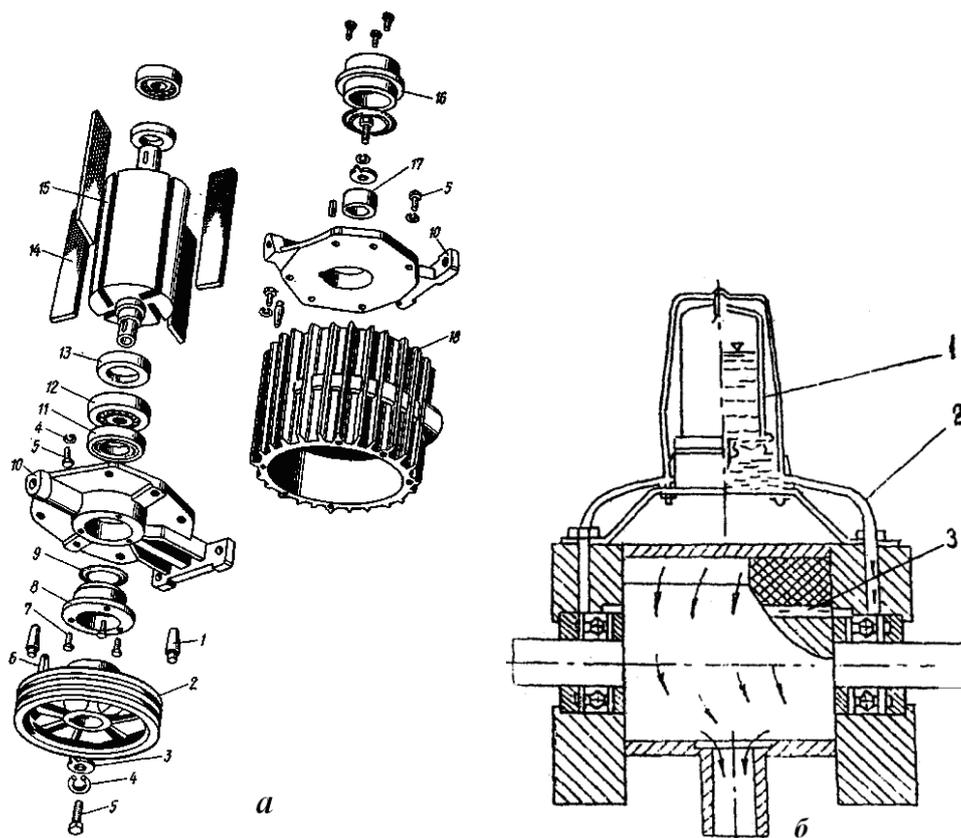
Детали вакуумного насоса УВУ-60/45 (а) и схема смазки насоса (б): а: 1 – штифт; 2 – шкив; 3 – стопорная шайба; 4, 13 – шайбы; 5 – болт; 6 – шпонка; 7 – винт; 8, 10, 16 – крышки; 9 – прокладка; 11 – манжета; 12 шарикоподшипник; 14 – лопатка; 15 - ротор; 17 втулка; 18 – корпус
